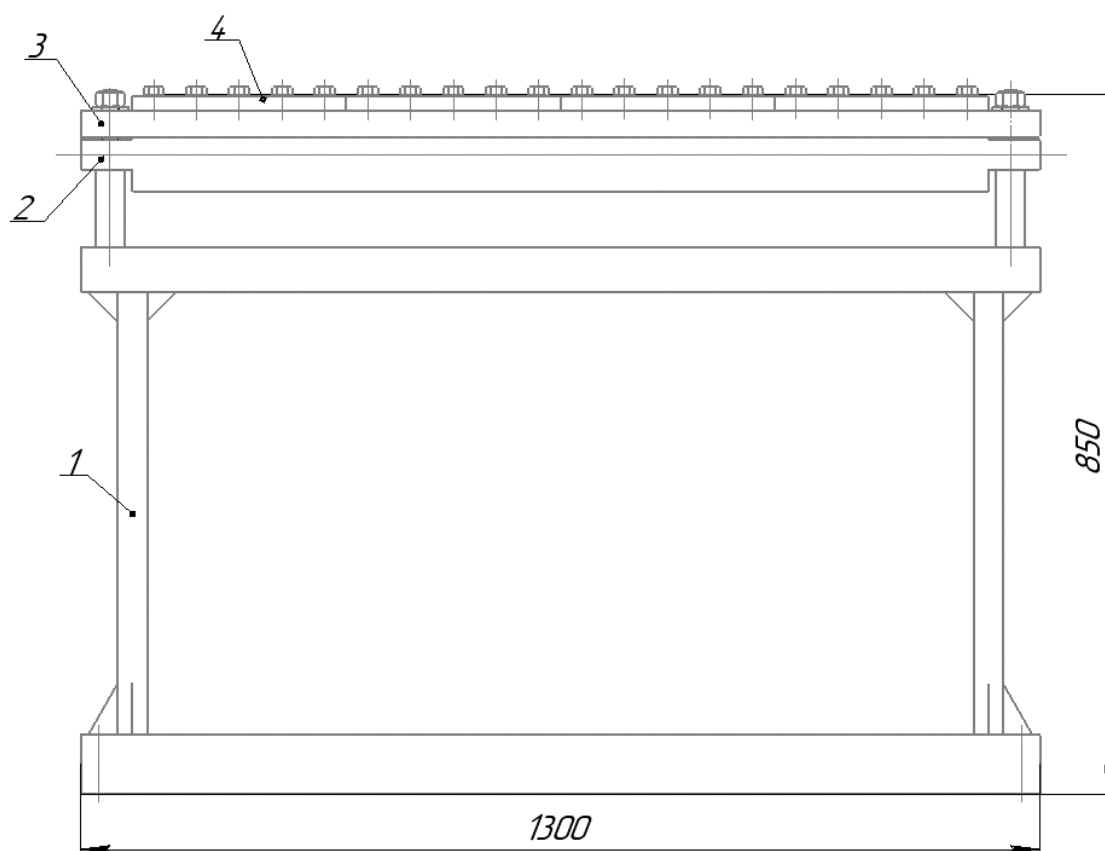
Сборочное приспособление. 1 - станина; 2 - балка (с теплоотводящей медной подкладкой); 3 – рамка; 4 - прижимные пластины.
